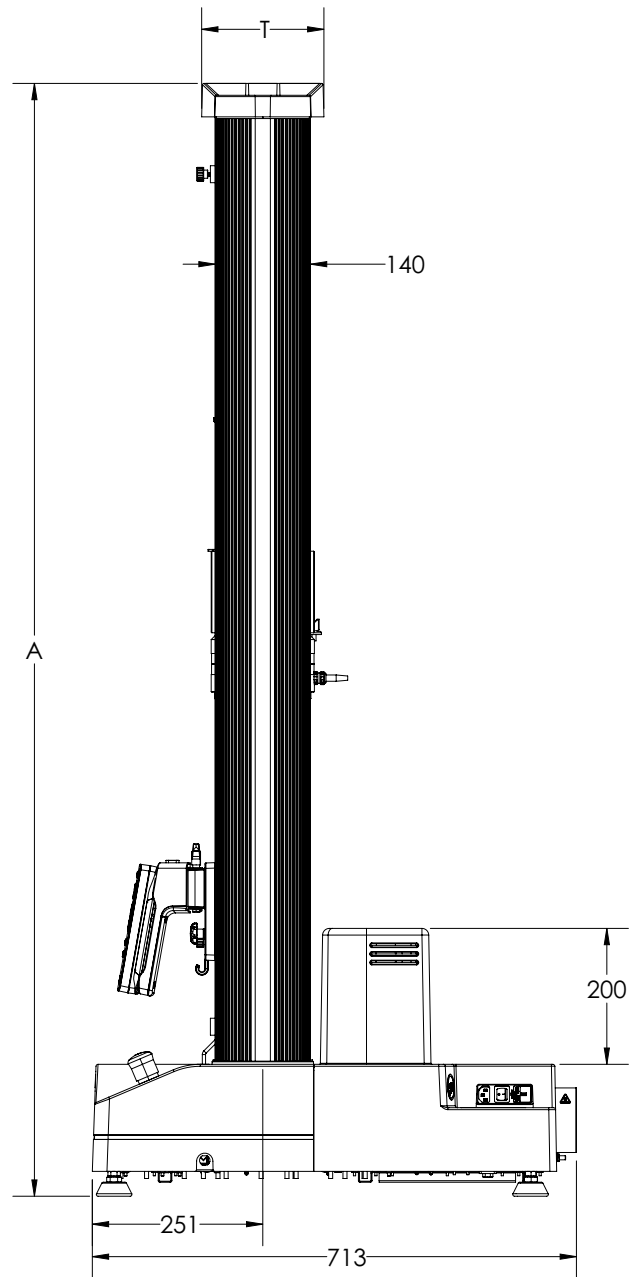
68TM-100 dimensões da estrutura - vista lateral
